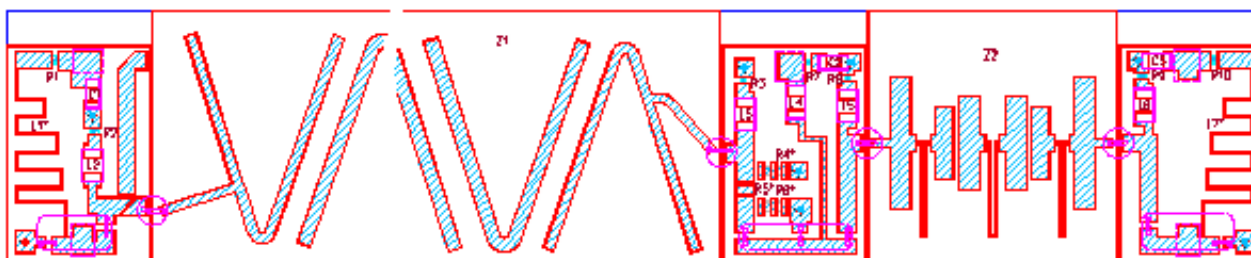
Сборочный чертёж узла полосового фильтра
